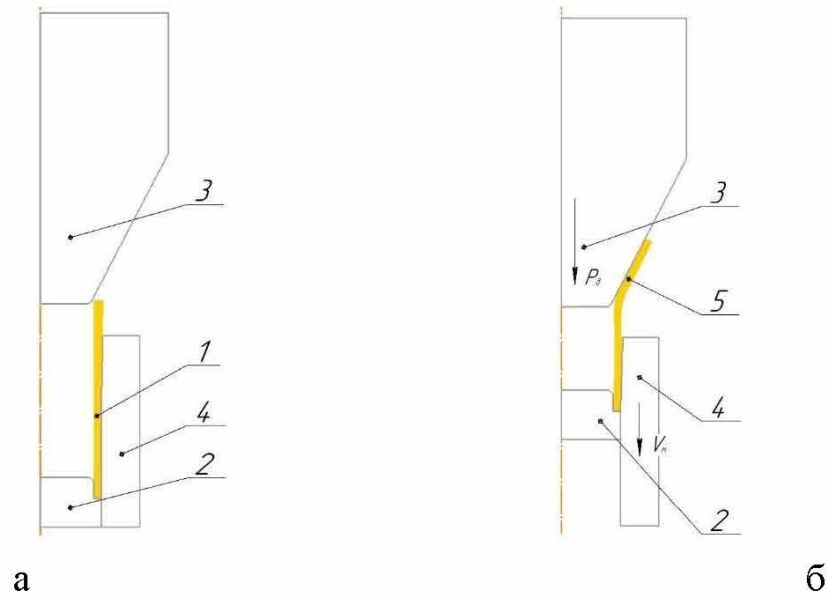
Схема процесу роздачі трубної заготовки:
